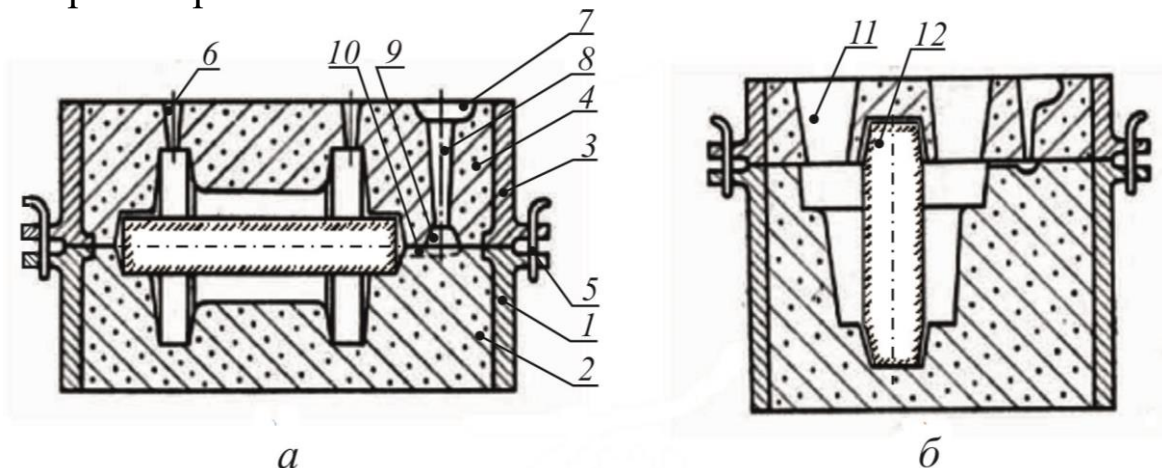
Литейные формы в сборе: 1 – нижняя опока; 2 – нижняя полуформа; 3 – верхняя опока; 4 – верхняя полуформа; 5 – центрирующие штыри; 6 – выпор; 7 – литниковая чаша; 8 – стояк; 9 – шлакоуловитель; 10 – питатель; 11 – прибыль; 12 – стержень
